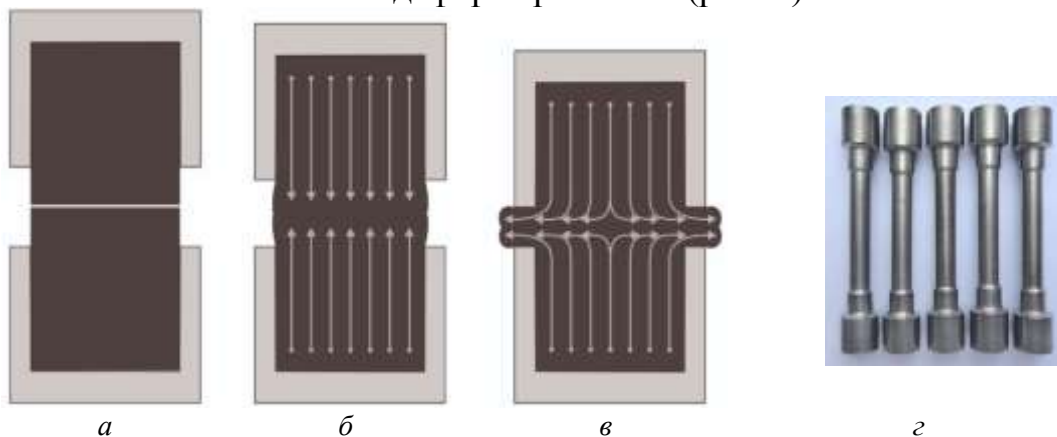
Основные стадии процесса моделирования свариваемых заготовок: форма заготовки после 1-ой (а), 2-ой (б) и 3-ой (в) стадии и образцы, вырезанные из сваренных заготовок (г)
